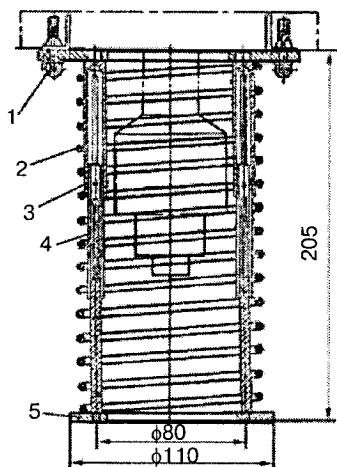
Телескопічна огорожа до свердлильного верстата:
